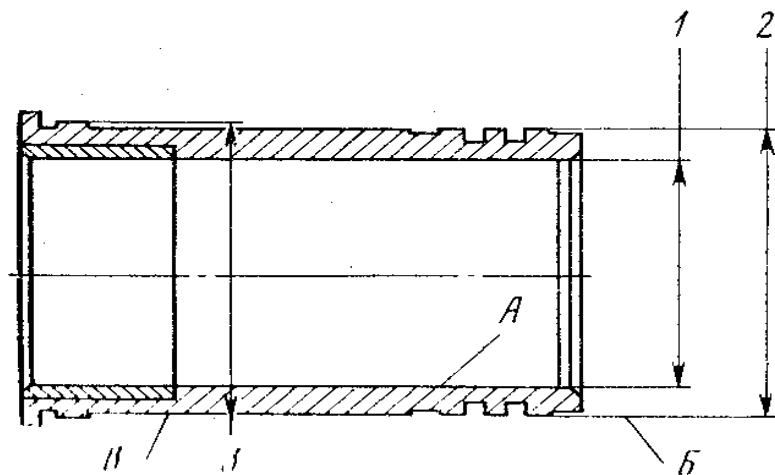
Гильза цилиндров двигателя ЗИЛ
